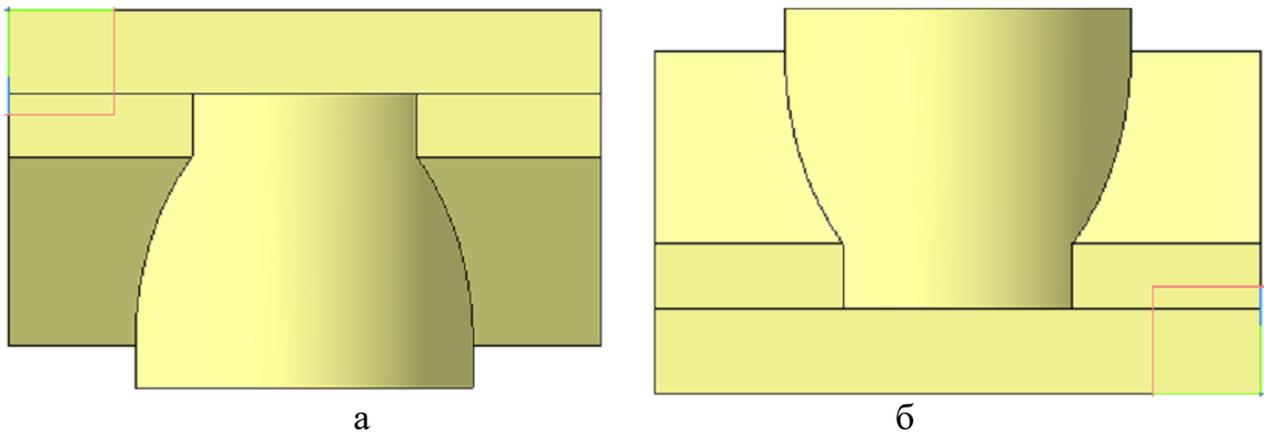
Поворот детали в удобное для *Главного вида* положение
